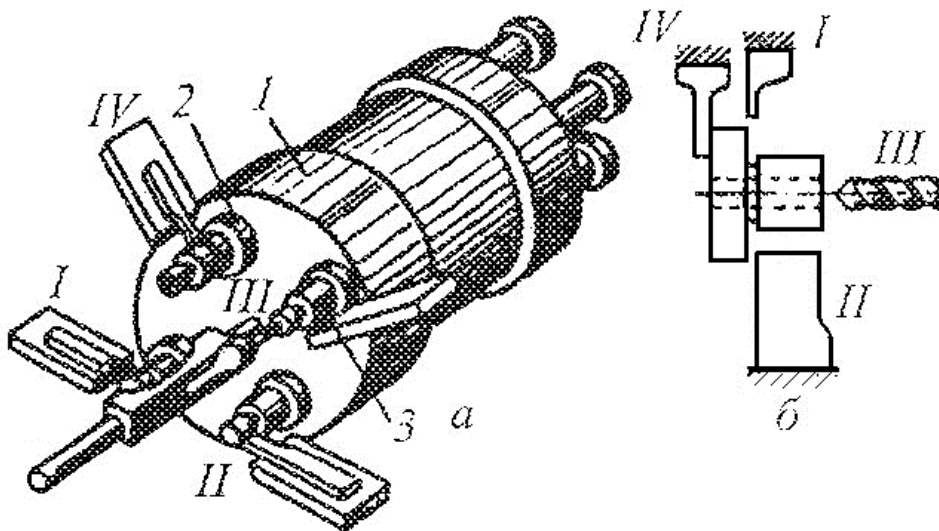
Схема до обробки заготовок на багатошпиндельному горизонтальному автоматі
